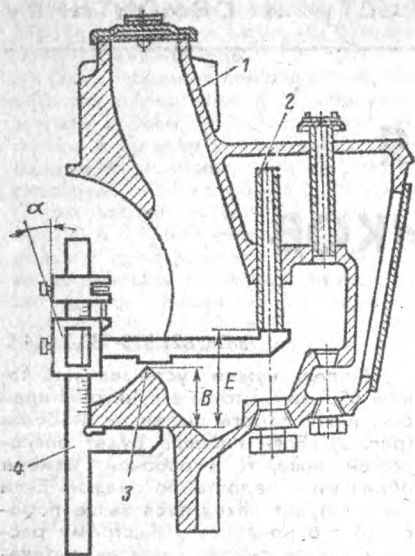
Проверка высоты установки ниппеля и высоты порожка шапки:
